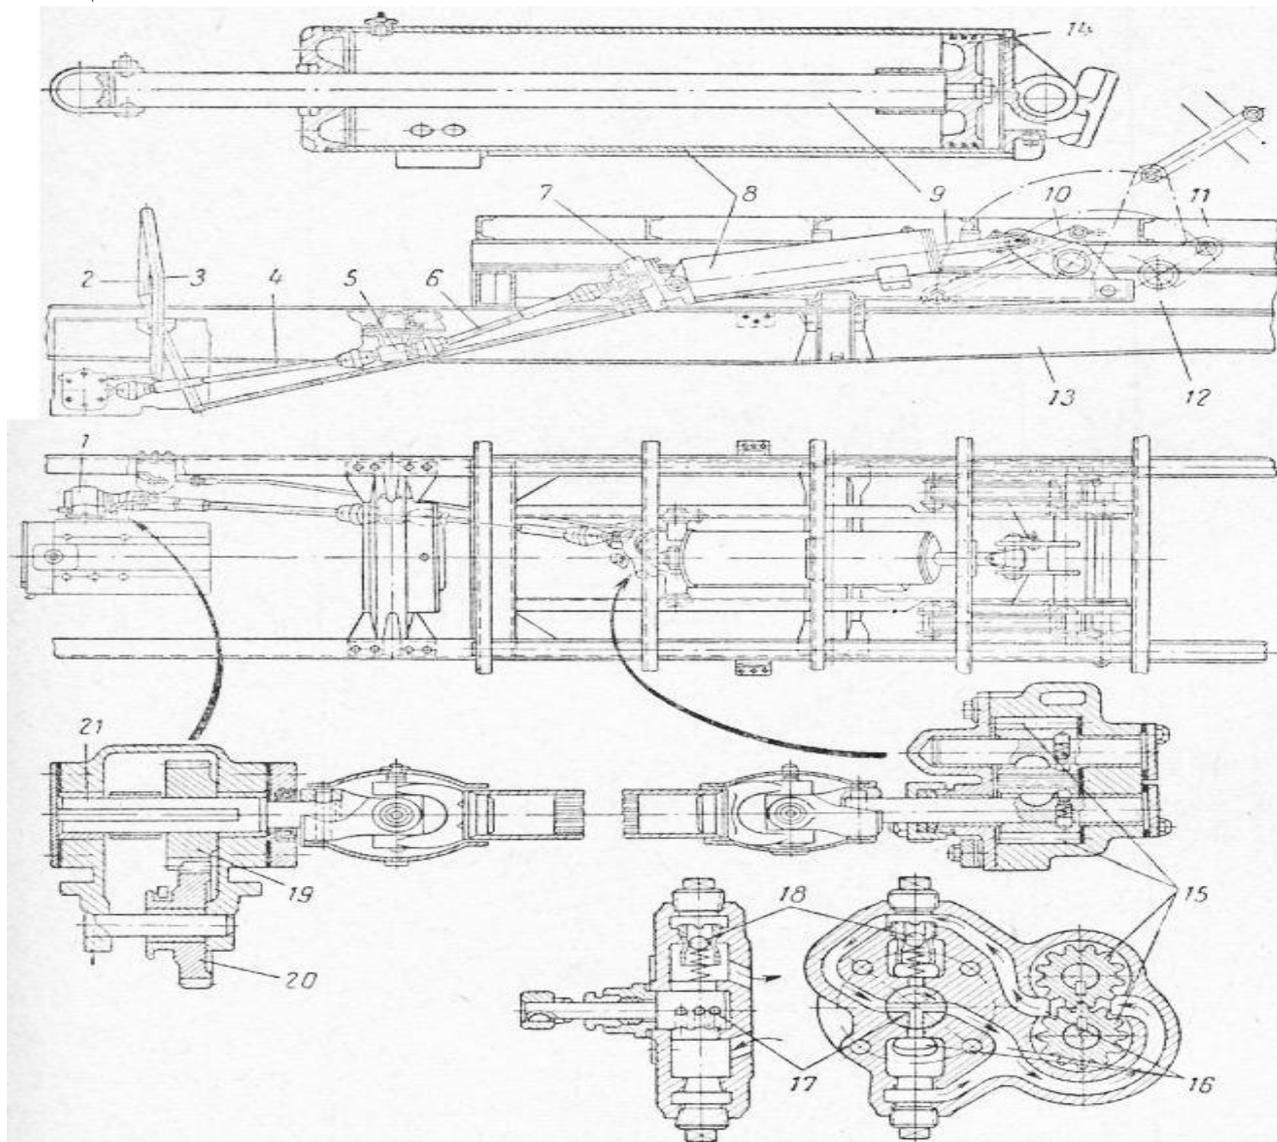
Подъемный механизм кузова автомобиля-самосвала МАЗ-205:
